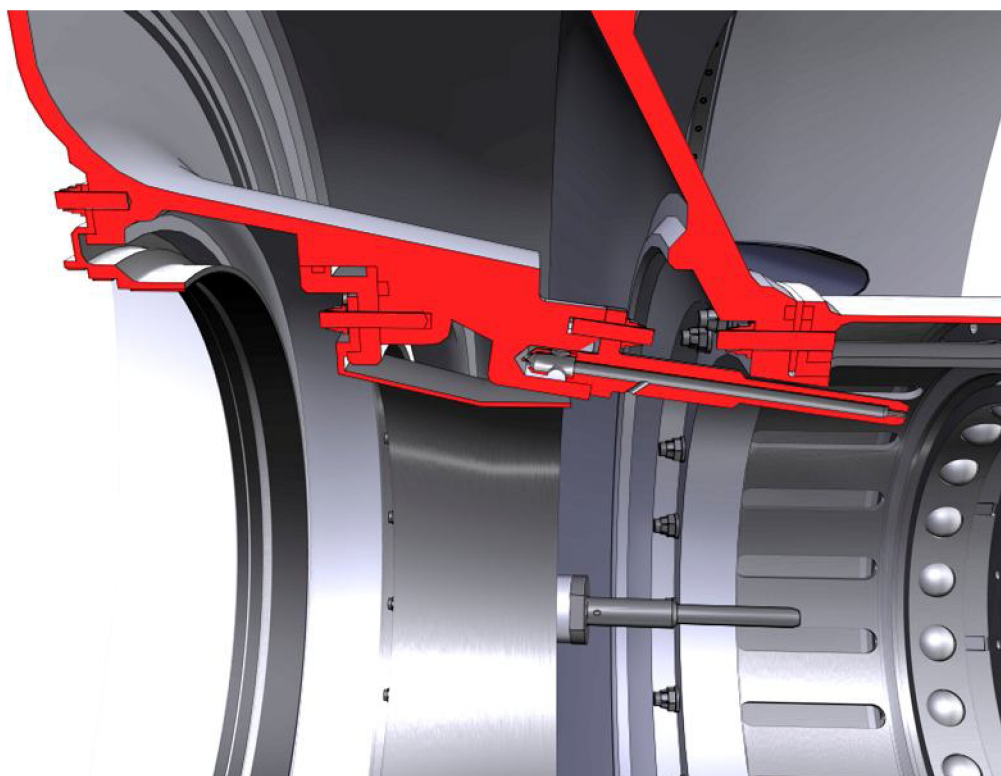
Промежуточный корпус (сечения по стойкам)
